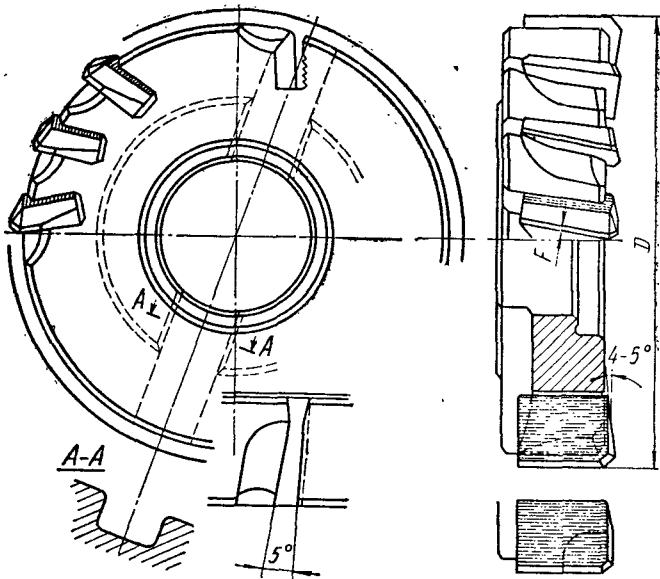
Торцовая фреза с клиновидными рифлеными ножами
